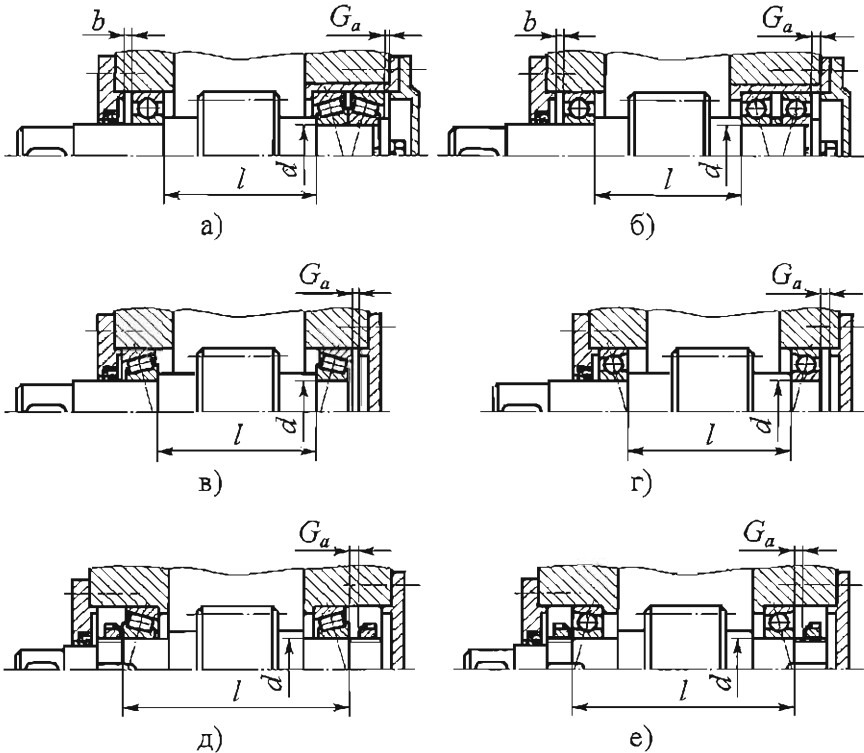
Конструктивные схемы установки подшипников качения в опорах валов:
